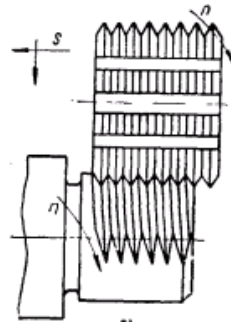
Обробка різьби гребінчастою фрезою
